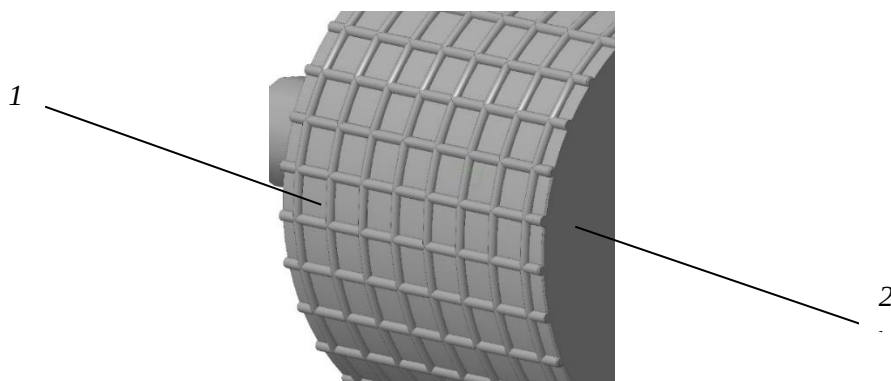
Усовершенствованный бандаж вала четырёхвалковой дробилки кокса
